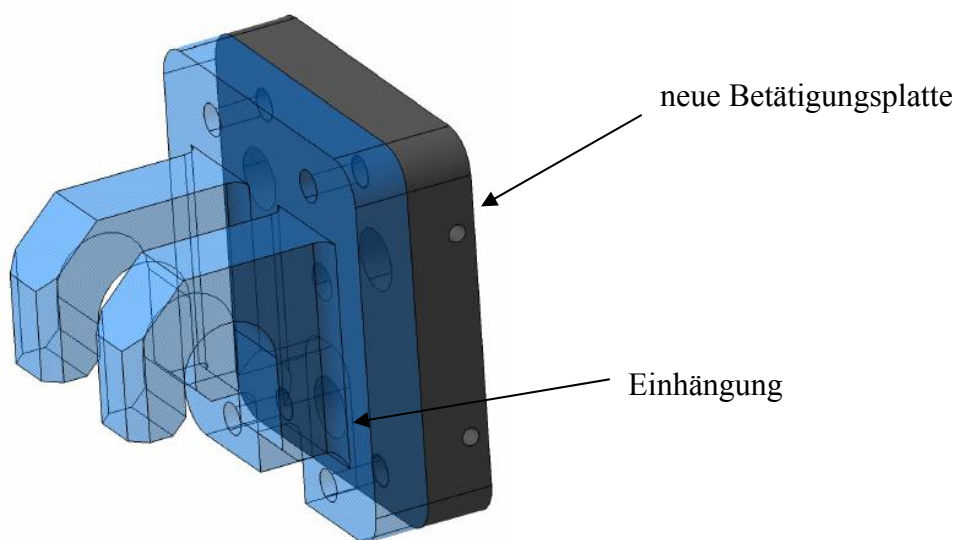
Betätigungsbaugruppe für Handset ²⁹
